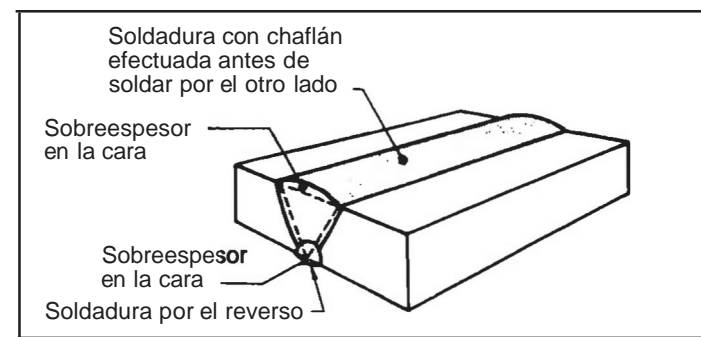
SOLDADURA POR EL REVERSO
